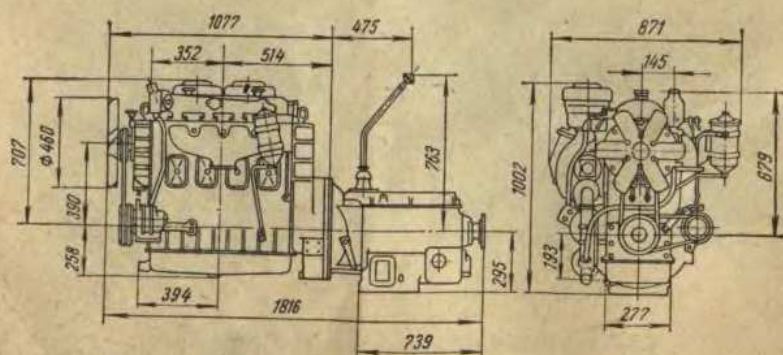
Габаритные размеры двигателей ЯАЗ-М204А и ЯАЗ-М204В
